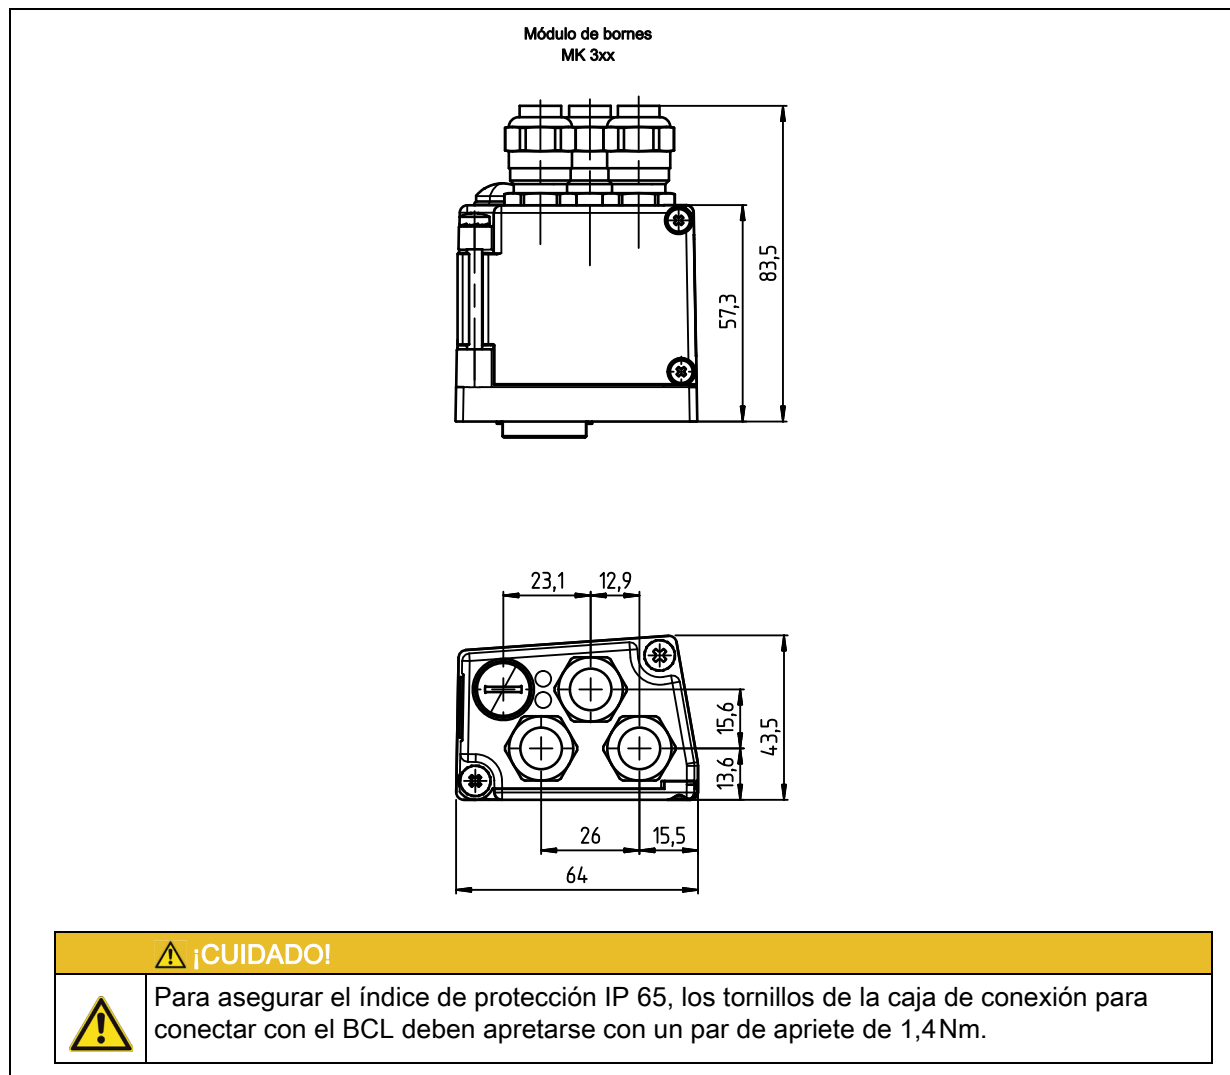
Dibujo acotado del módulo de bornes MK 3xx
